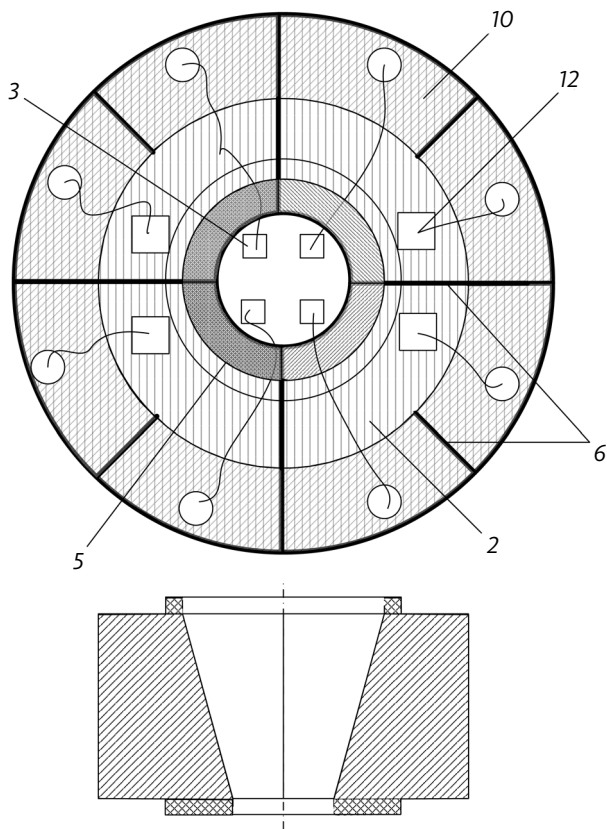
Чертеж (вид сверху) светодиодной ячейки
